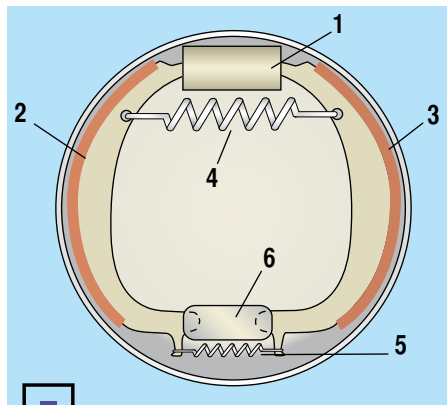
Механизм с плавающими колодками: 1 – колесный цилиндр; 2 – накладка передняя; 3 – накладка задняя; 4 – верхняя стяжная пружина; 5 – нижняя стяжная пружина; 6 – опорная стойка колодок
